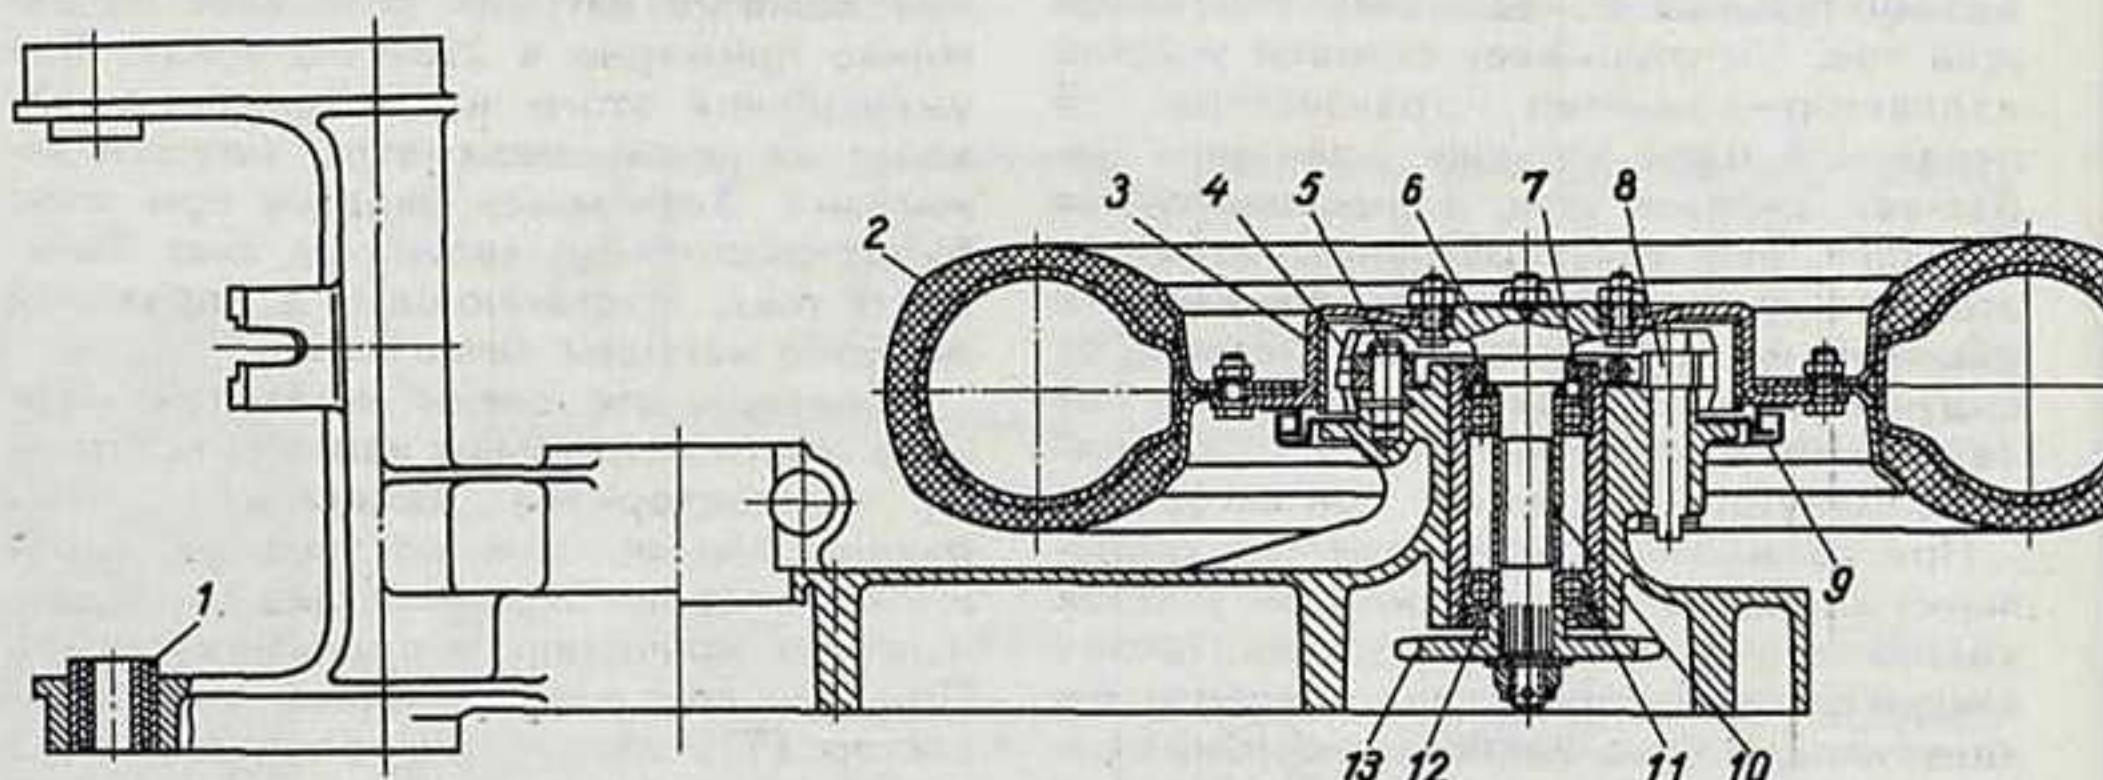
Алюминиевый литой рычаг и устанавливаемое на нем заднее колесо: 1 — резиново-карбоновый подшипник; 2 — шина; 3 — стальной тормозной барабан; 4 — тормозные колодки; 5 — ось тормозных колодок; 6 — ось заднего колеса; 7 — сальник; 8 — тормозной кулачок с осью; 9 — лабиринтное уплотнение; 10 — распорная втулка; 11 — подшипник; 12 — гайка; 13 — ведомая звездочка заднего колеса.
